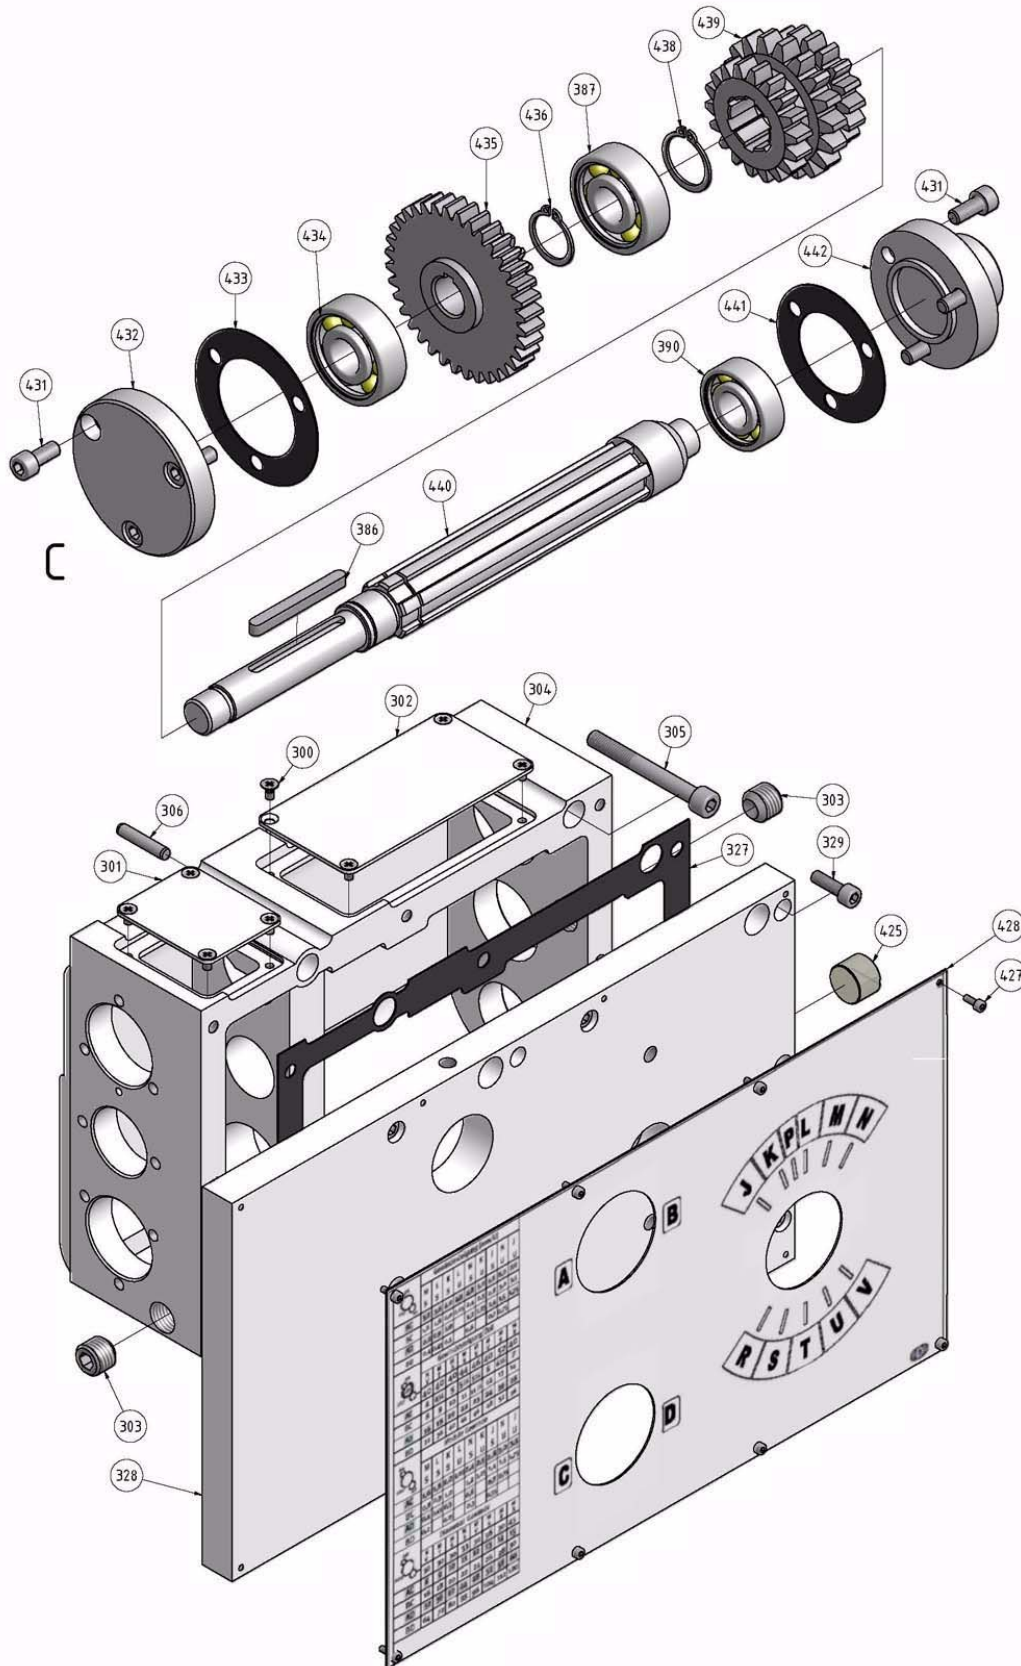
Vorschubgetriebe 3-4 - Feed gear 3-4
